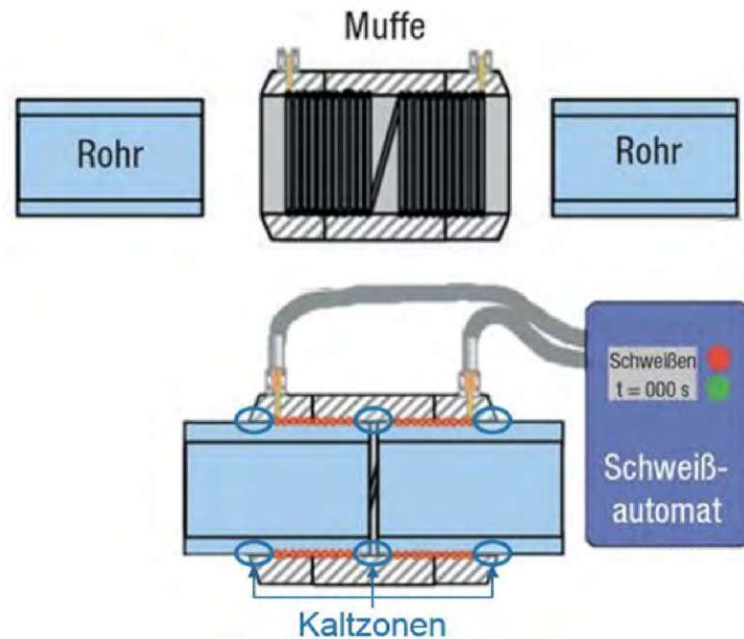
Prinzipbild für das Elektroschrumpfschweißen [25]
